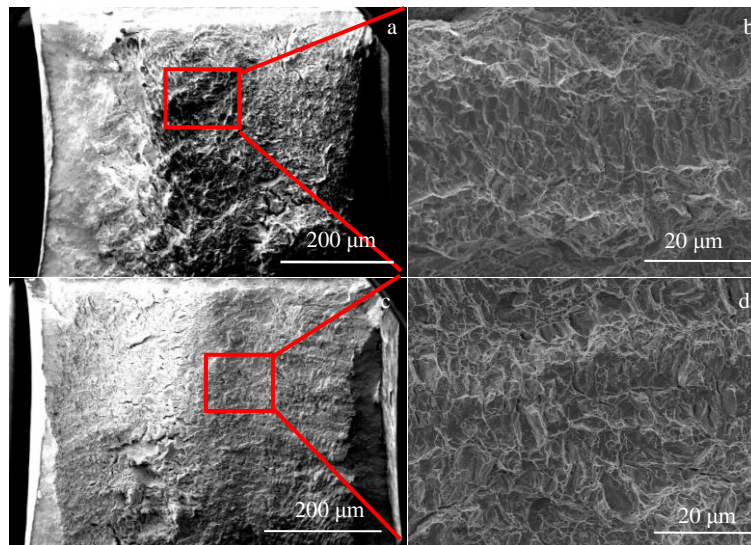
2 种保护气体下焊接接头的冲击断口形貌
